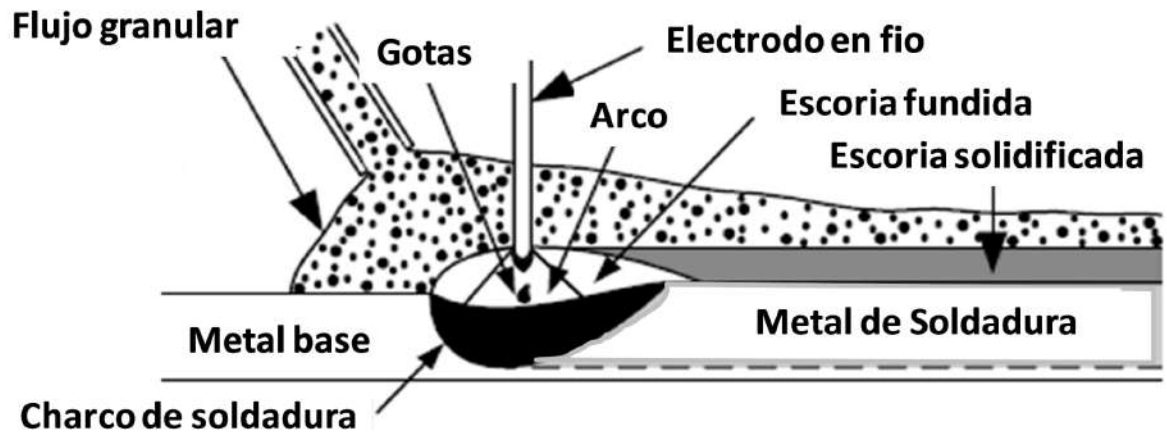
esquema de soldadura SAW, fuente: "SciELO Brasil"
